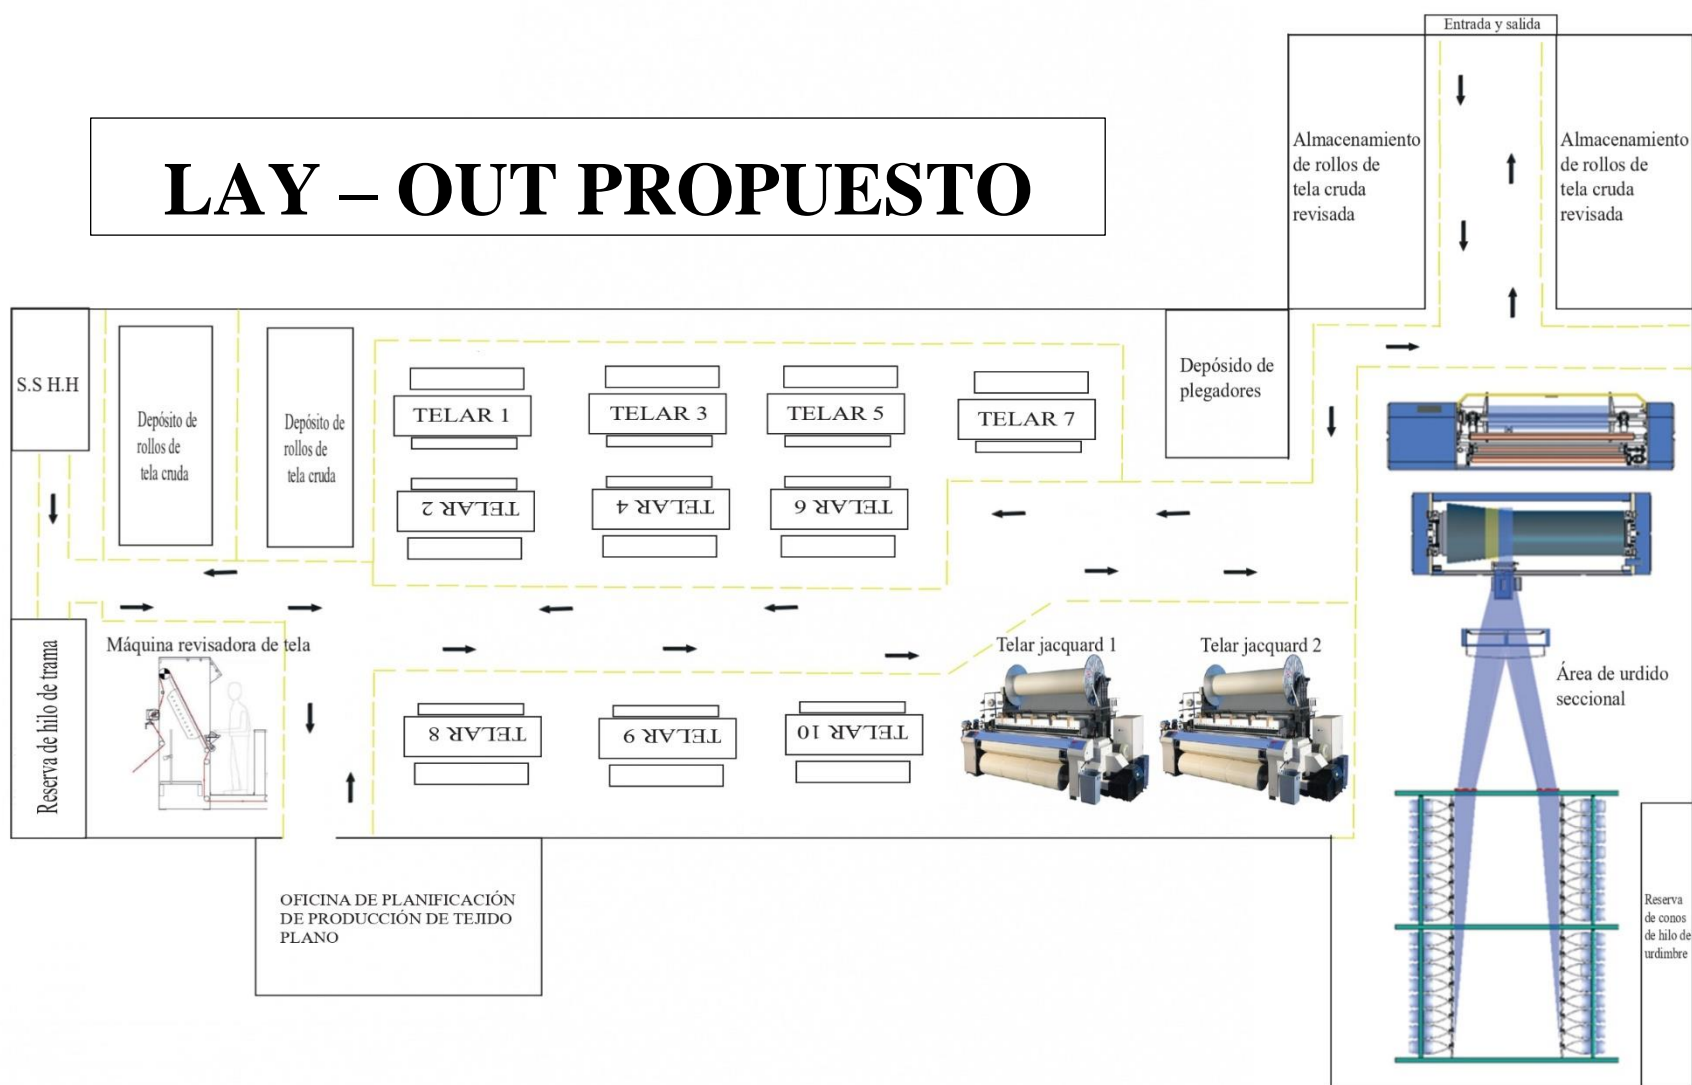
LAY-OUT – Propuesto para el Área de Tejeduría Plana
